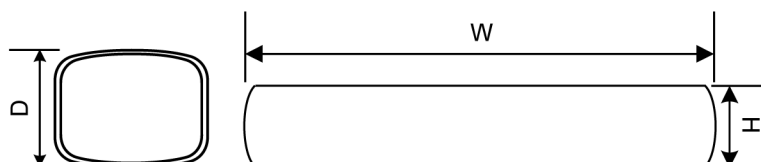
Skematisk fremstilling, dimensioner i millimeter
